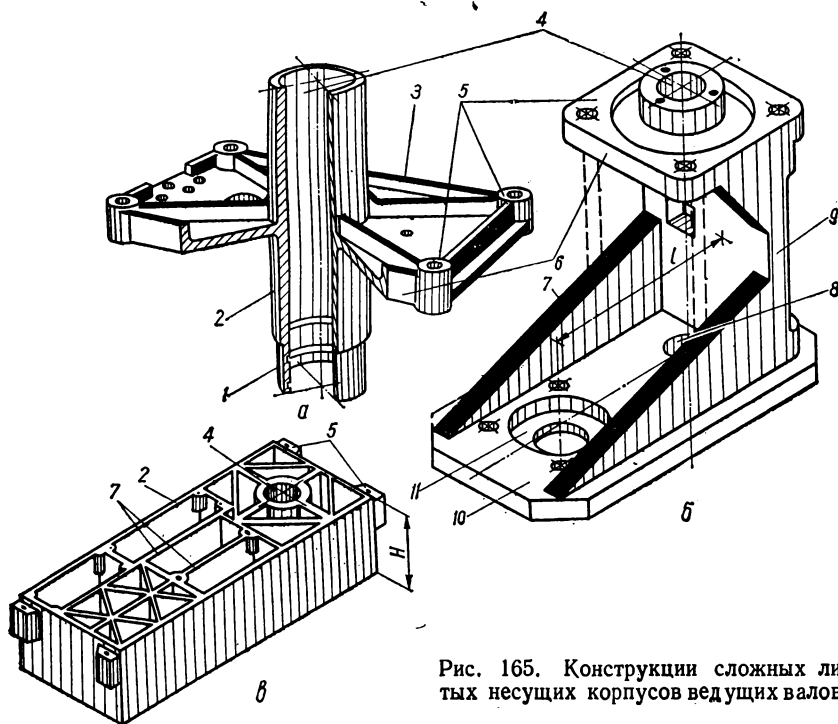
Конструкции сложных литых несущих корпусов ведущих валов.
